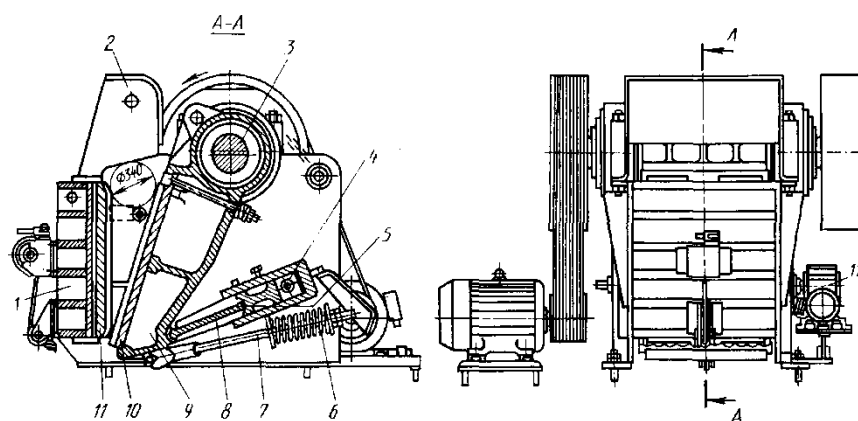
Щековая дробилка со сложным движением щеки
